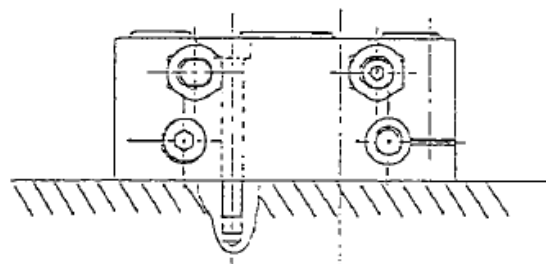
Befestigung von oben (mit Innensechskantschraube)
